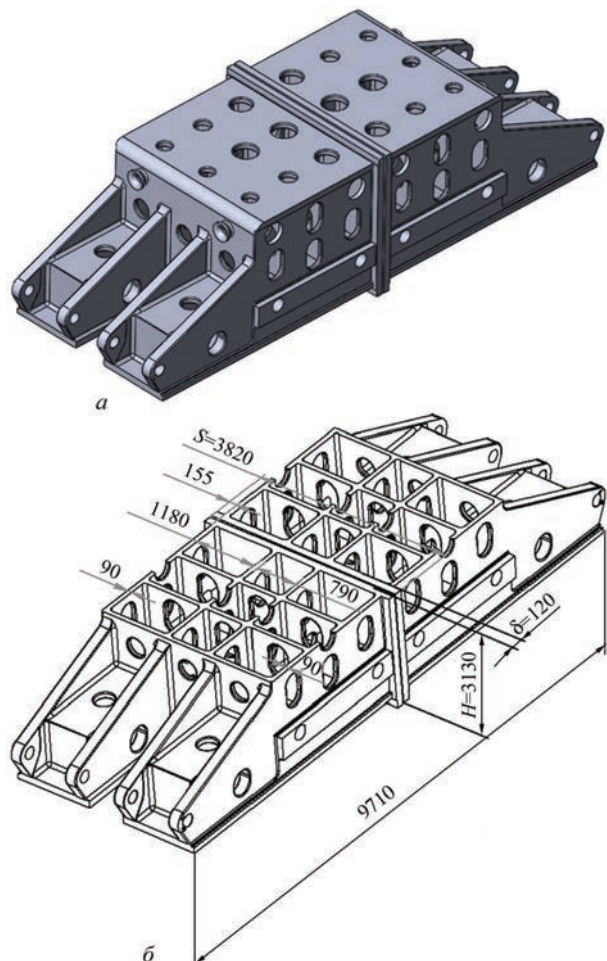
Конструкция средней части станины ковочного гидравлического пресса усилием 70/90 МН: а — общий вид; б — структурная схема
